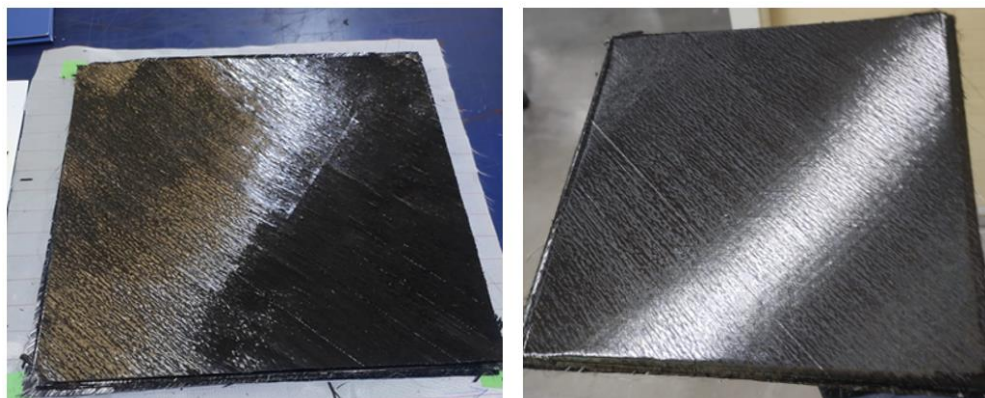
Процесс сборки вакуумного мешка для подформовки
